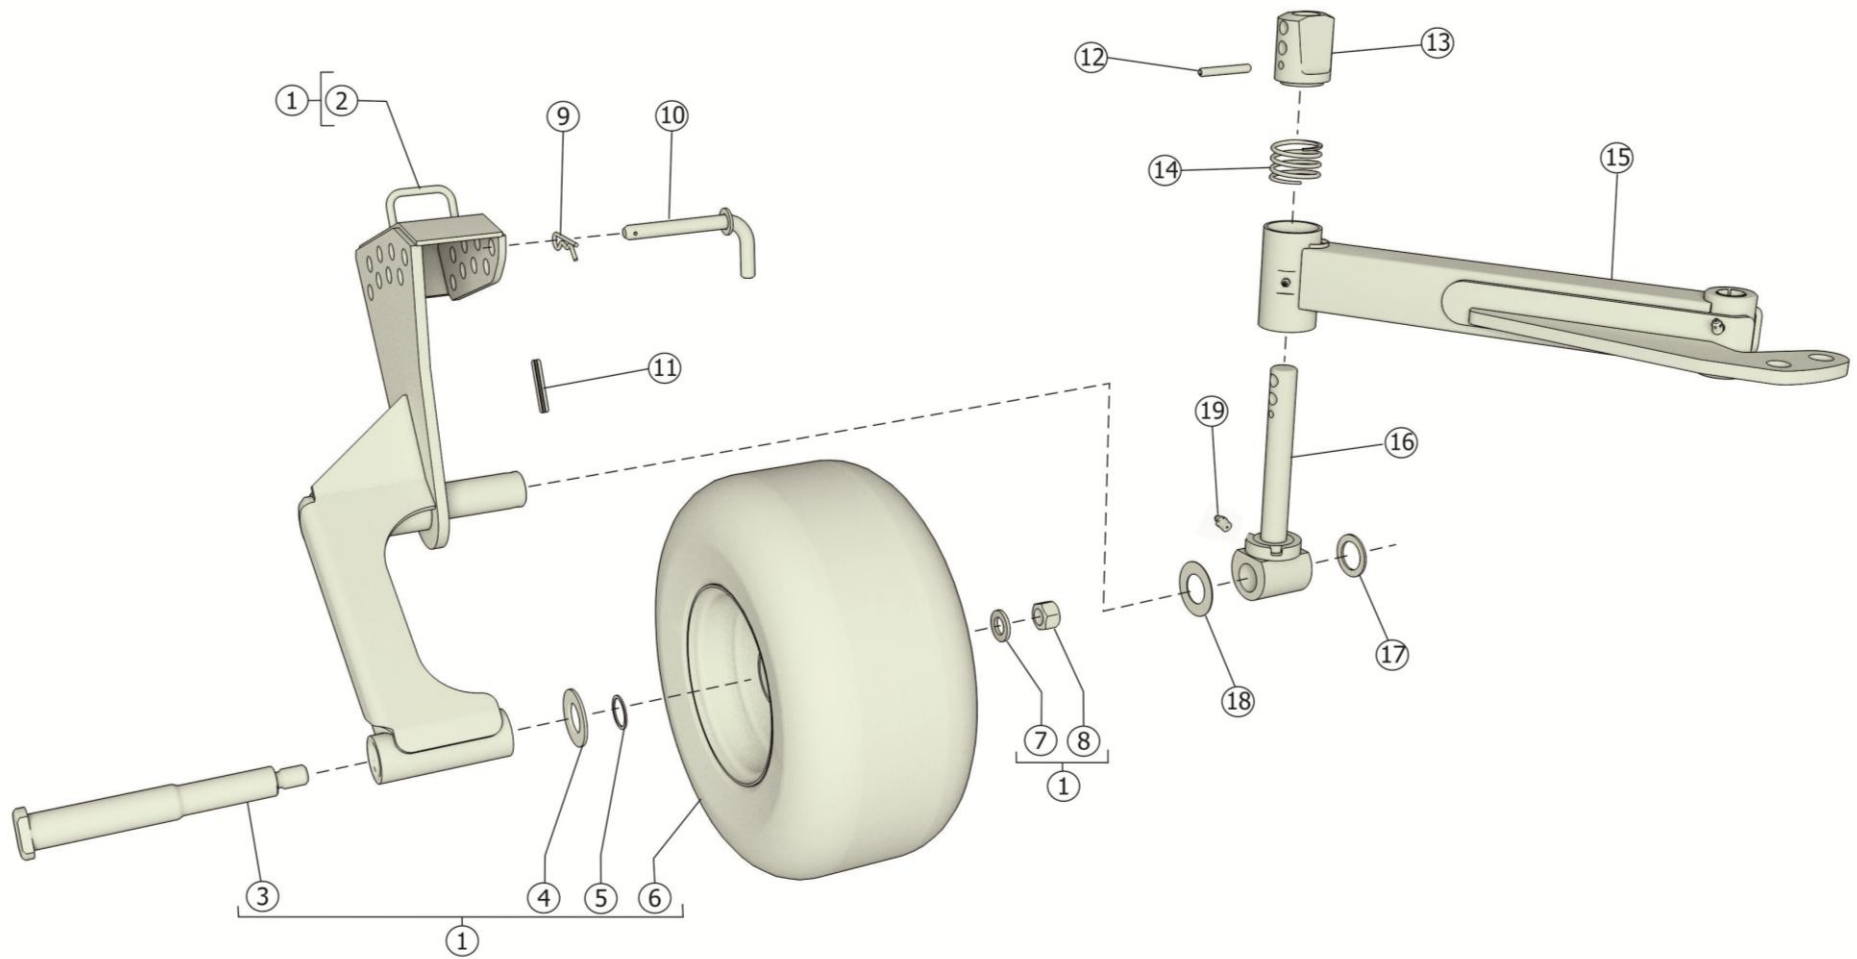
Колесо флюгерное ПК-300.01.04.000А
